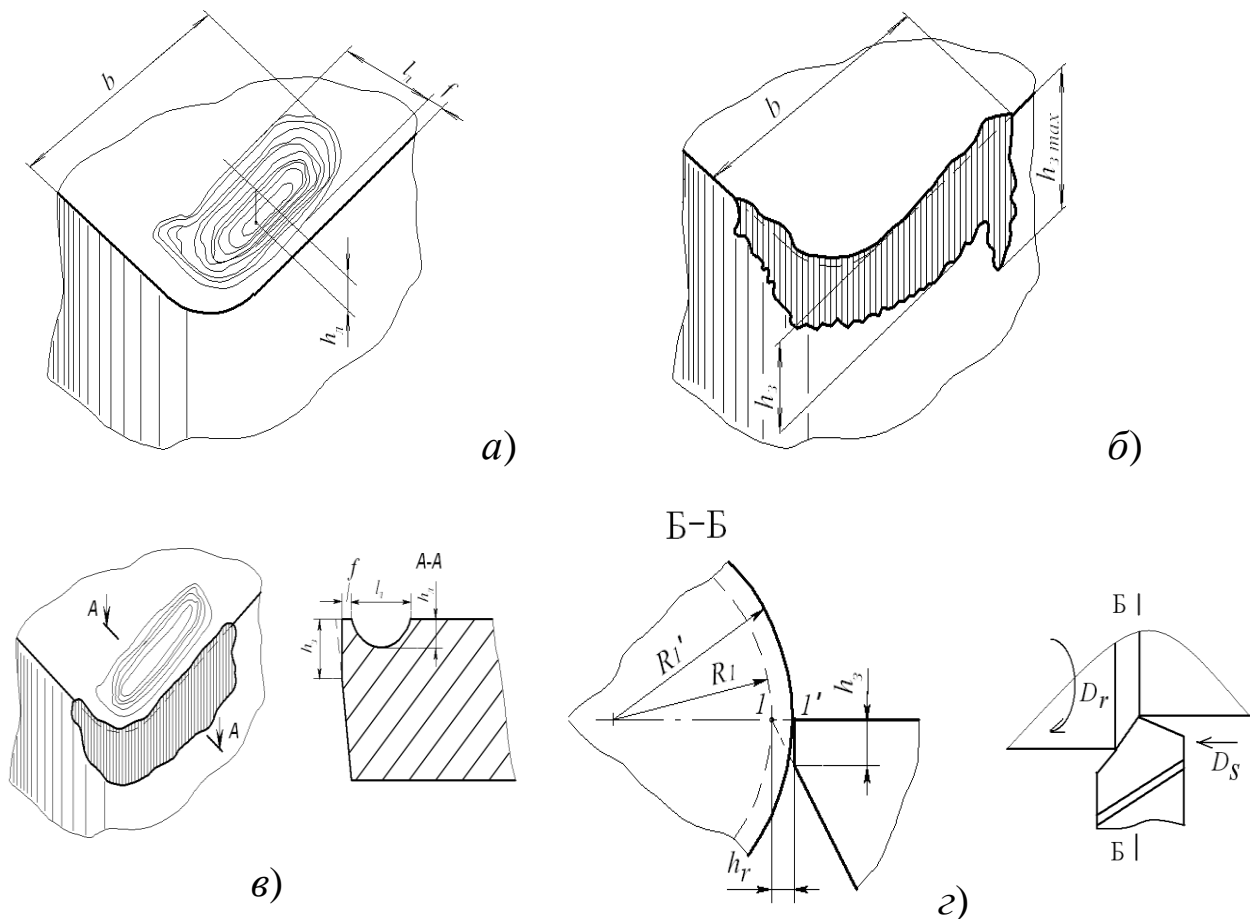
Износ резца по передней (*а*), задней (*б*) поверхностях; сбалансированный износ резца (*в*); радиальный износ резца (*з*)
